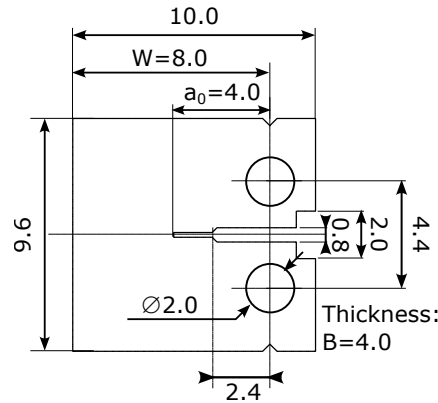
Dimensions de l'éprouvette mini-C(T)
